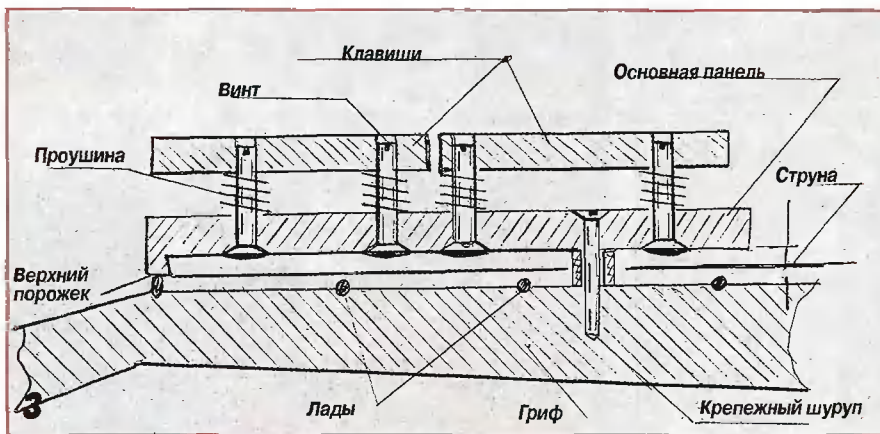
Гитарная приставка в разрезе. Вид сбоку.
